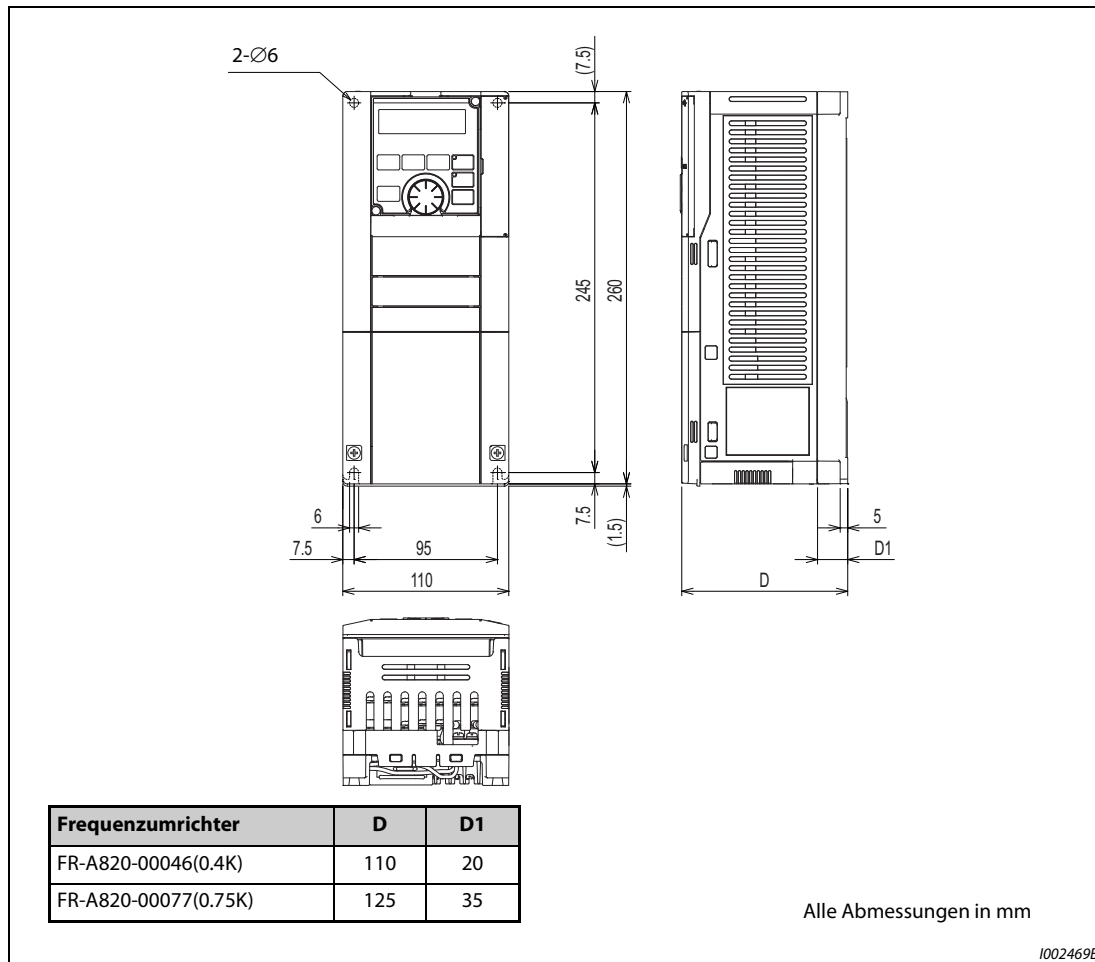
Abmessungen der Frequenzumrichter FR-A820-00046(0.4K) und FR-A820-00077(0.75K)
